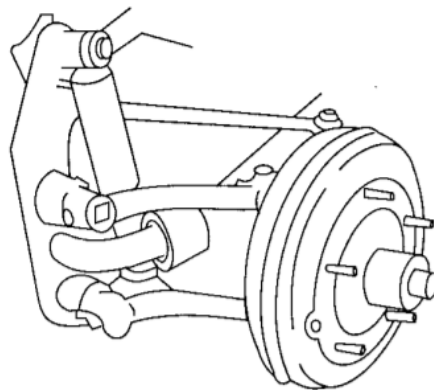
Suspensão Trailing arm dianteira independente (Fonte: GILLESPIE, 1992, p. 242)
